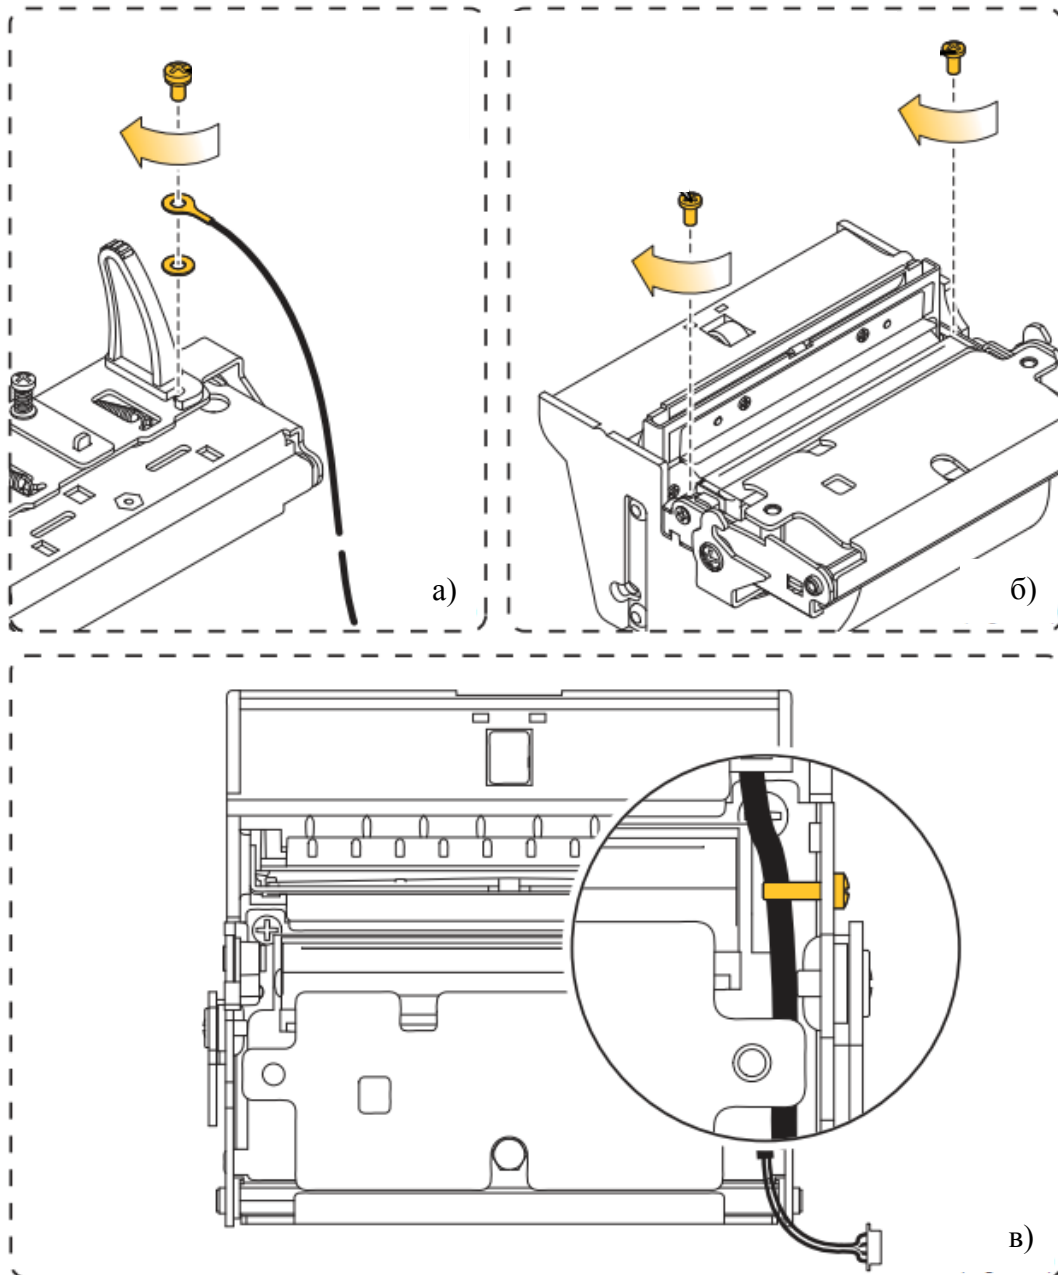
Присоединение механизма термопечати к верхней крышке
